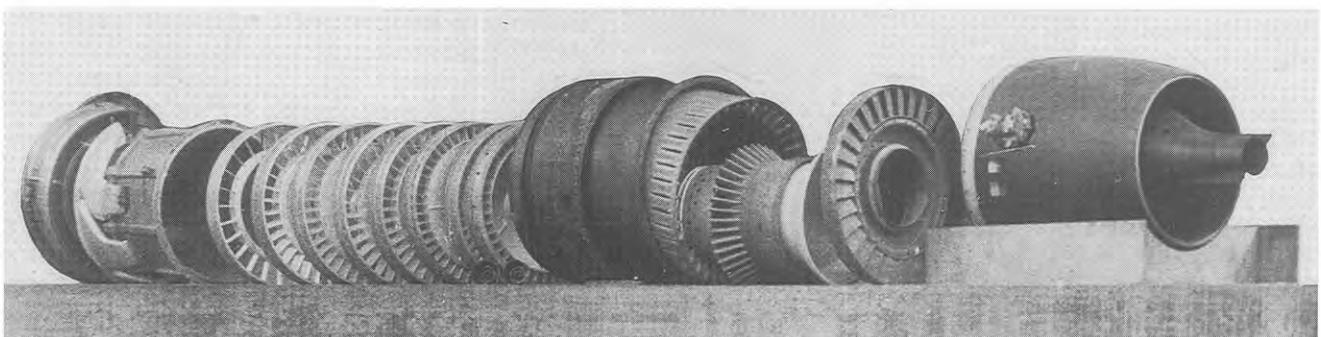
При изготовлении узлов турбореактивного двигателя БМВ 109-003 использовалось большое количество листового металла, который также применялся для изготовления обтекателя пускового двигателя и полых лопаток ротора турбины
